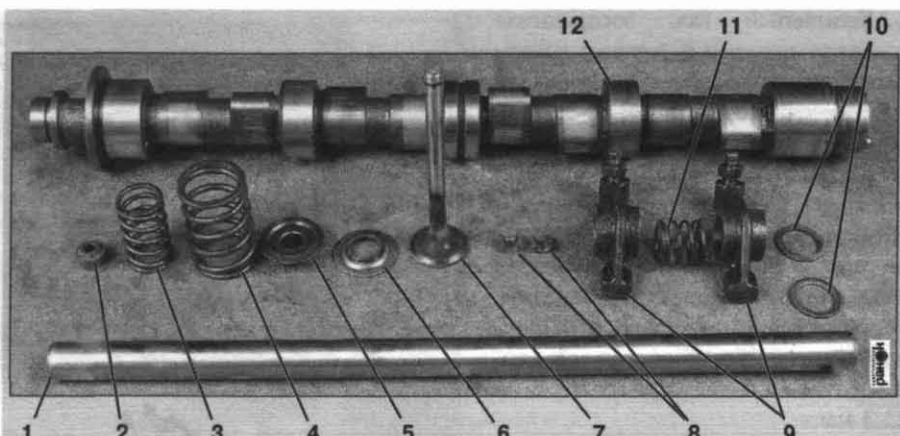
Детали газораспределительного механизма: 1 — ось коромысел; 2 — маслоотражательный колпачок (сальник клапана); 3 — внутренняя пружина клапана; 4 — наружная пружина клапана; 5 — тарелка клапана; 6 — опорная шайба клапана; 7 — клапан; 8 — сухари клапана; 9 — коромысла клапанов; 10 — шайбы оси коромысел; 11 — пружина оси коромысел; 12 — вал распределительный
